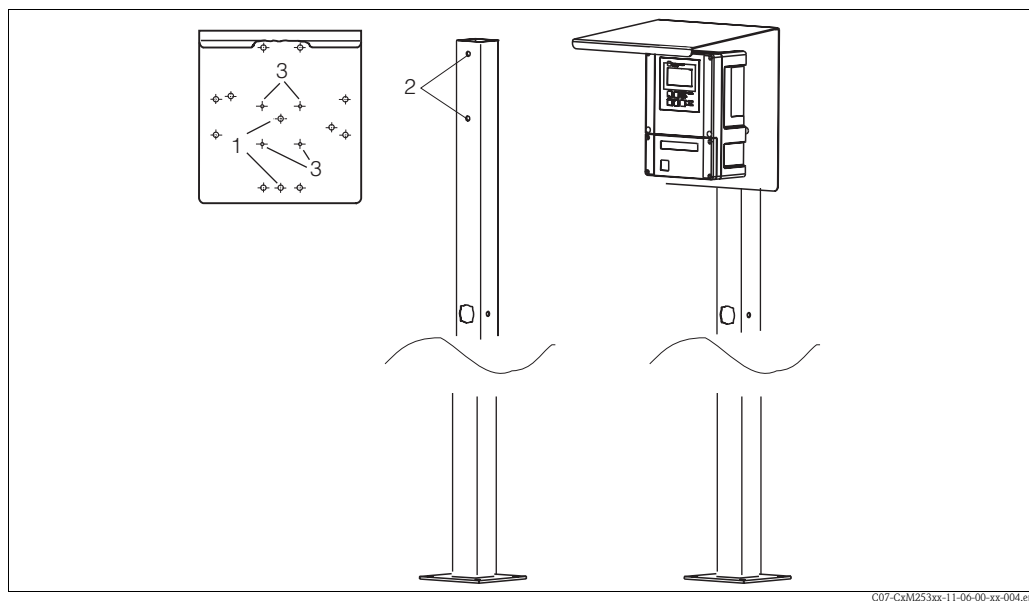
Przyrząd obiektowy zamontowany na stojaku do rur
